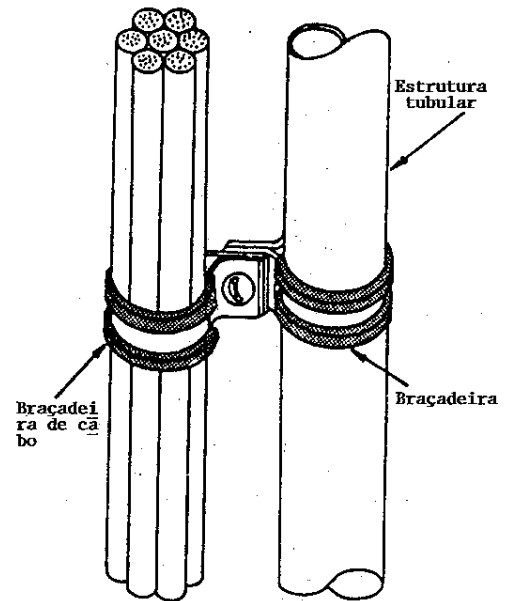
Instalação da braçadeira de cabo na estrutura tubular.
